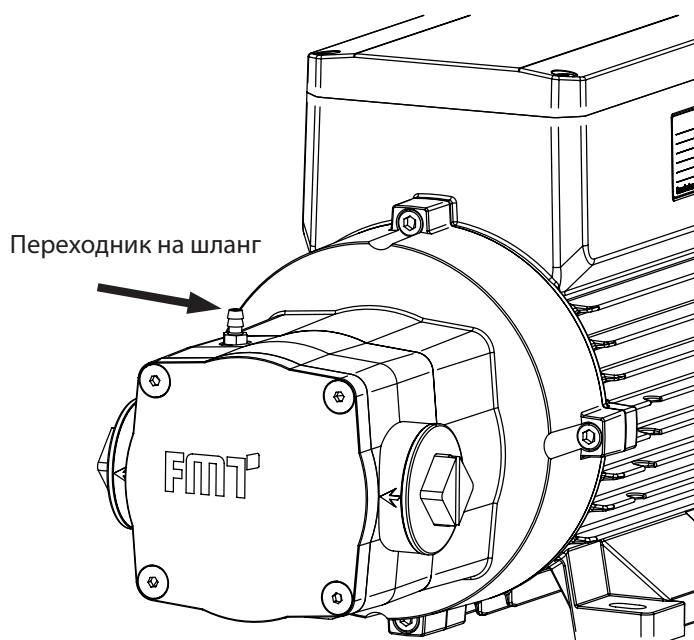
2: Резьбовая втулка с резьбой для защиты от протечек
